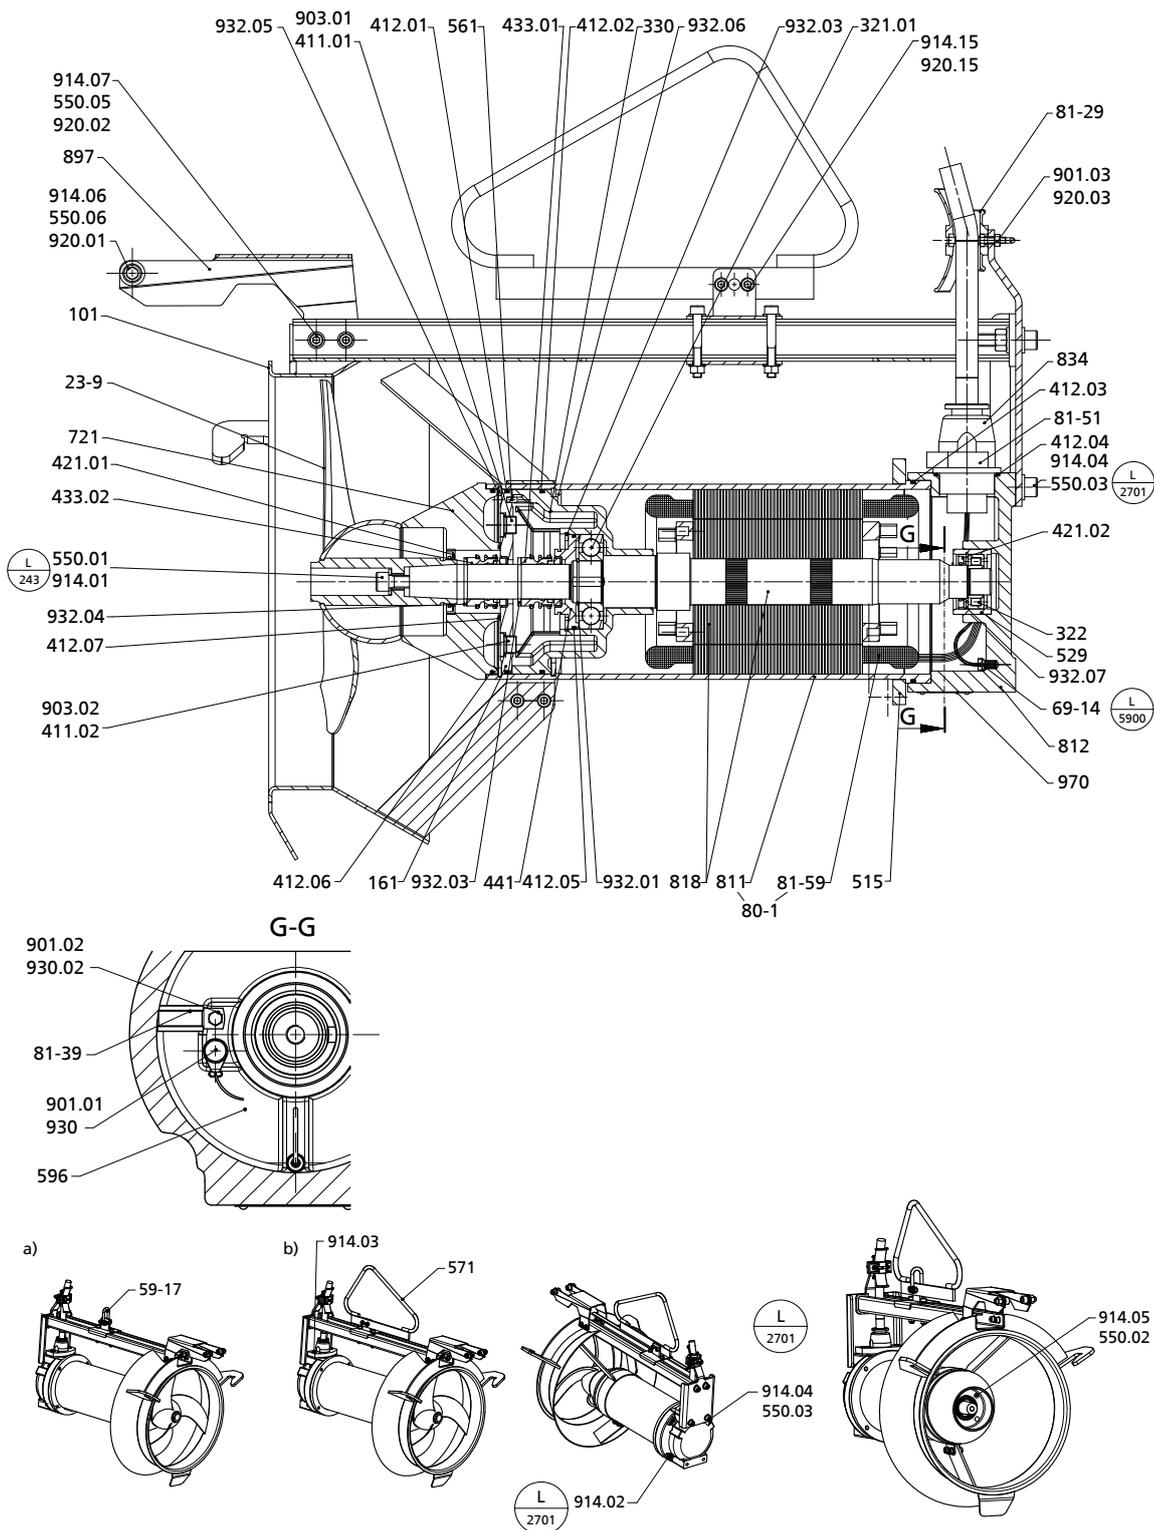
Чертеж общего вида: а) с серьгой б) со скобой (дополнительно)
